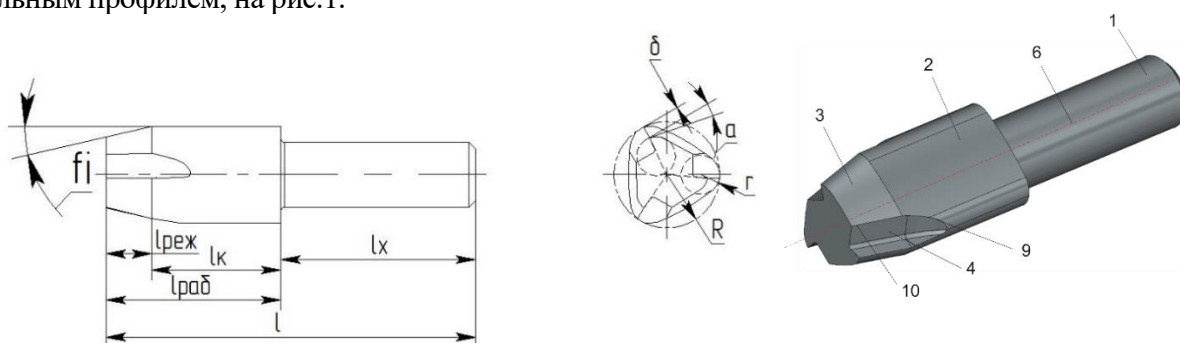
Комбинированный режуще-выглаживающий твердосплавный зенкер с гексагональным профилем
